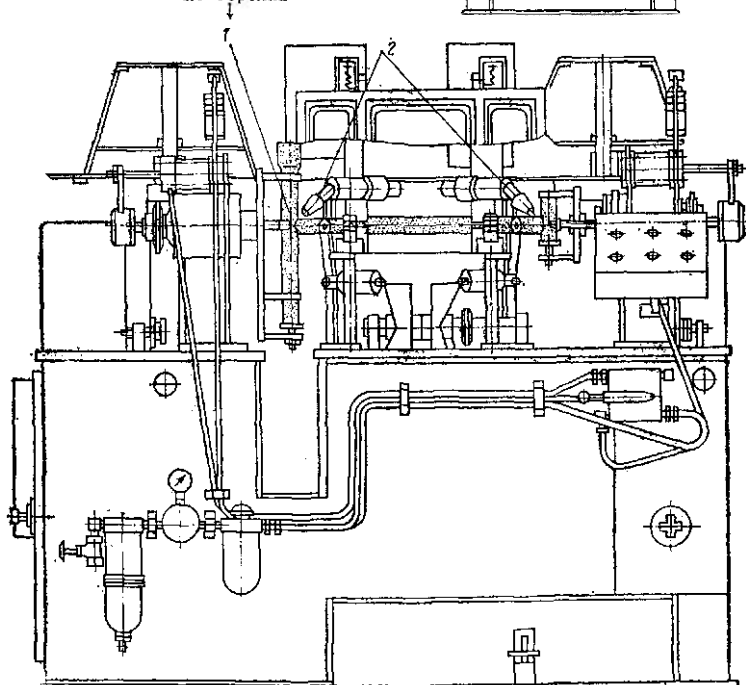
Полуавтомат для двусторонней сварки радиаторного узла СТД-557
